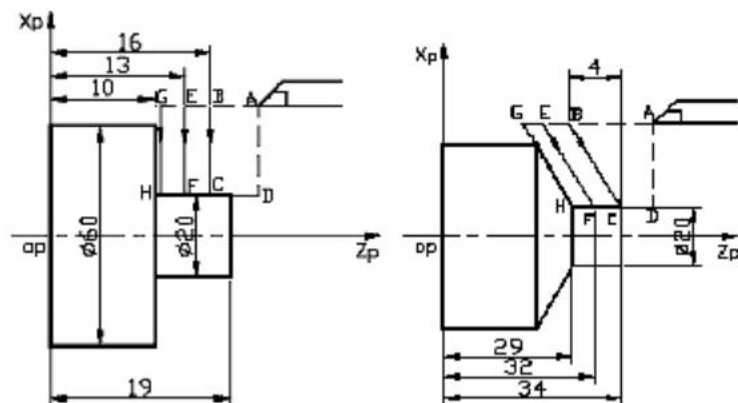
端面切削循环例题 图 3.26 带锥度的端面切削循环例题
